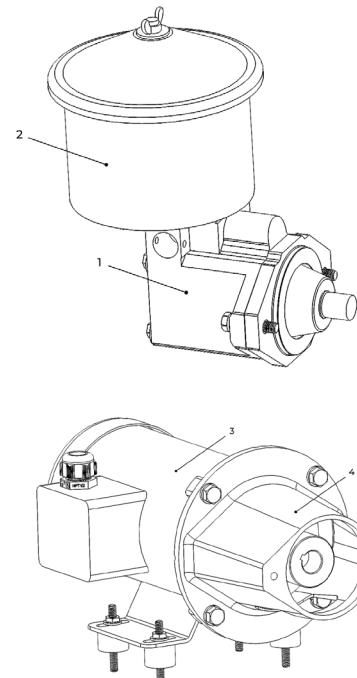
Assemblage de la pompe de direction (1) / réservoir intégré (2) et du moteur hydraulique à piston axial (3) / adaptateur moteur-différentiel (4).
